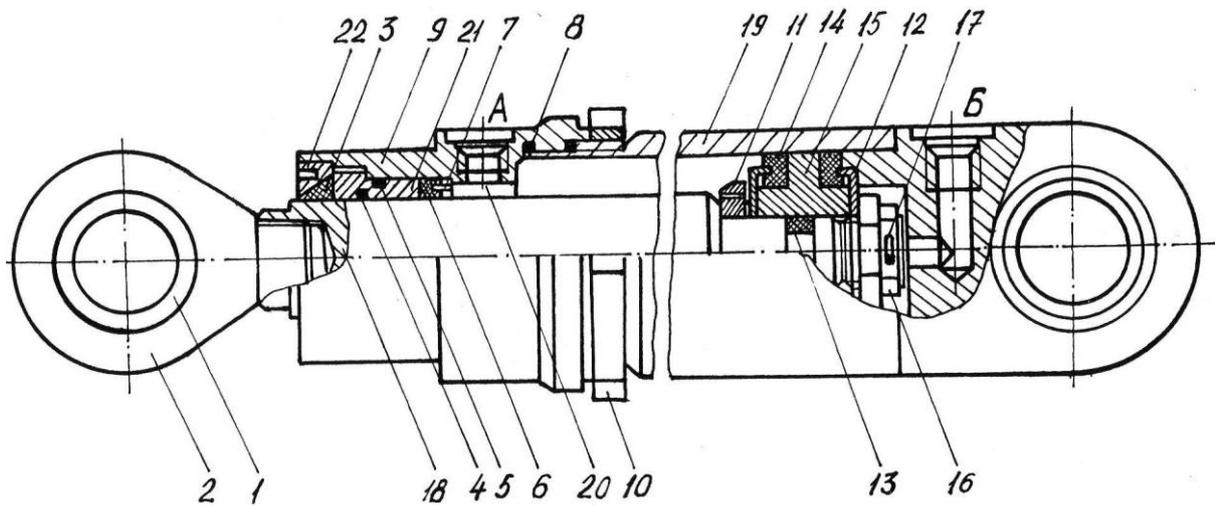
Гидроцилиндр: 1 – подшипник; 2 – проушина штока; 3 – грязесъемник; 4, 5, 8 и 13 – уплотнительные кольца; 6 – манжета штока; 7 и 12 – манжетодержатели; 9 – передняя крышка; 10 – контргайка; 11 – демпфер; 14 – манжеты поршня; 15 – поршень; 16 – гайка поршня; 17 – шплинт; 18 – шток; 19 – гильза гидроцилиндра с задней крышкой; 20 – кромка крышки; 21 – втулка передней крышки; 22 – гайка грязесъемника
